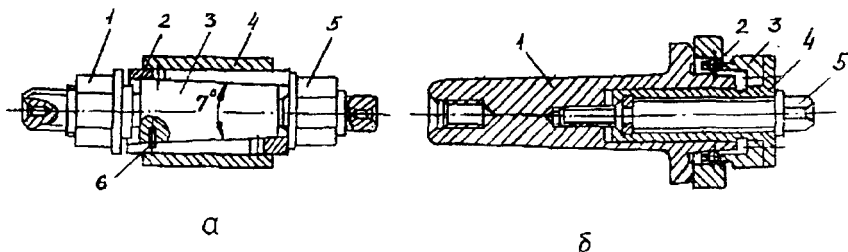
Разжимные оправки: а — цапговая, б — шариковая
